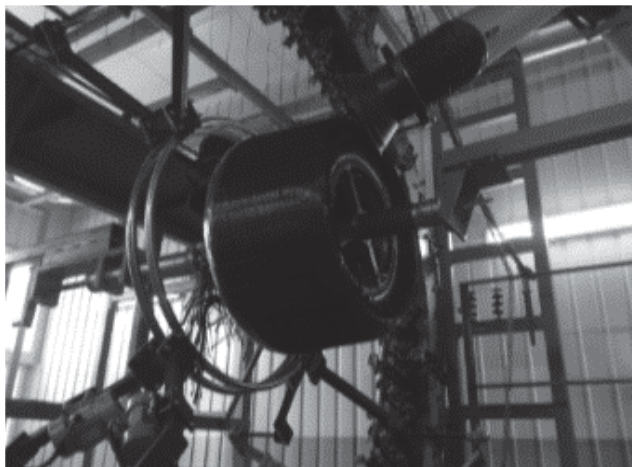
РП128-1-130 с установленной оплетаемой заготовкой
